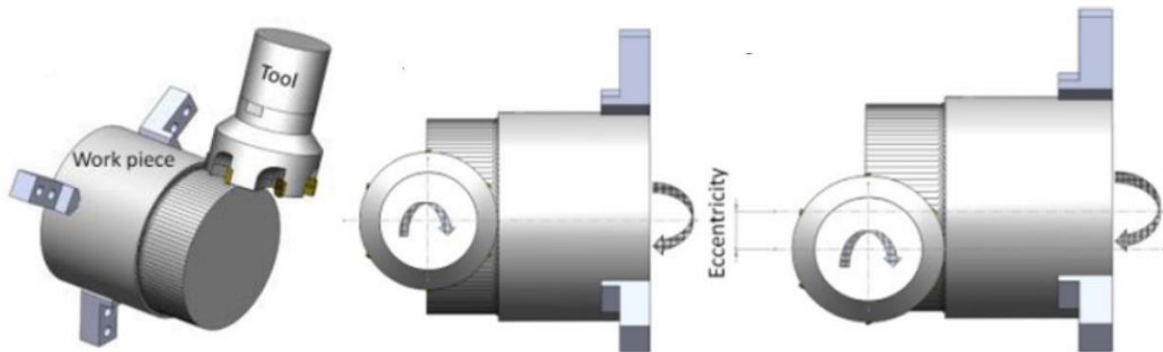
Комбінована операція токарно-фрезерного оброблення [20]
